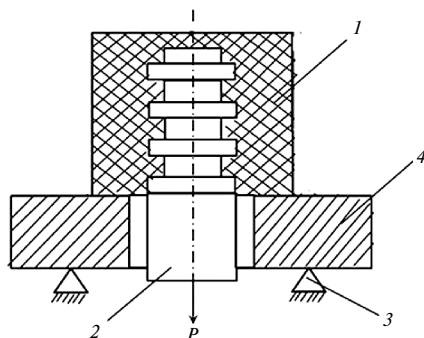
Испытание пластмассовой детали для прямоугольного резьбового образца: 1 – деталь из термопласта; 2 – металлический арматур; 3 – опора; 4 – приспособления.
